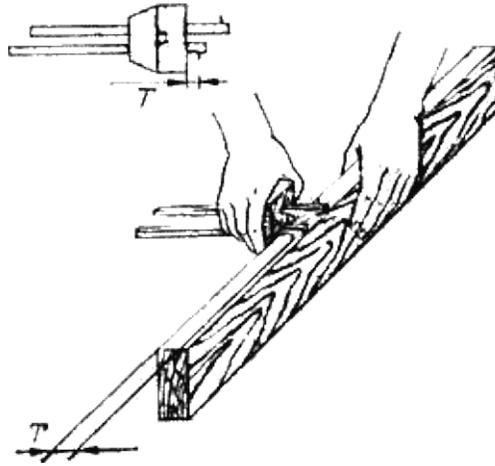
Разметка толщины заготовки с помощью рейсмуса
